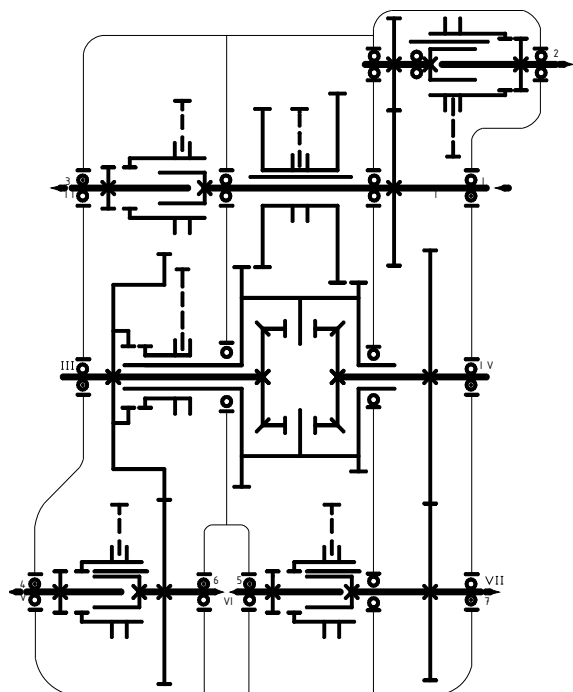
Раздаточная коробка БТР-80 (кинематическая схема)
